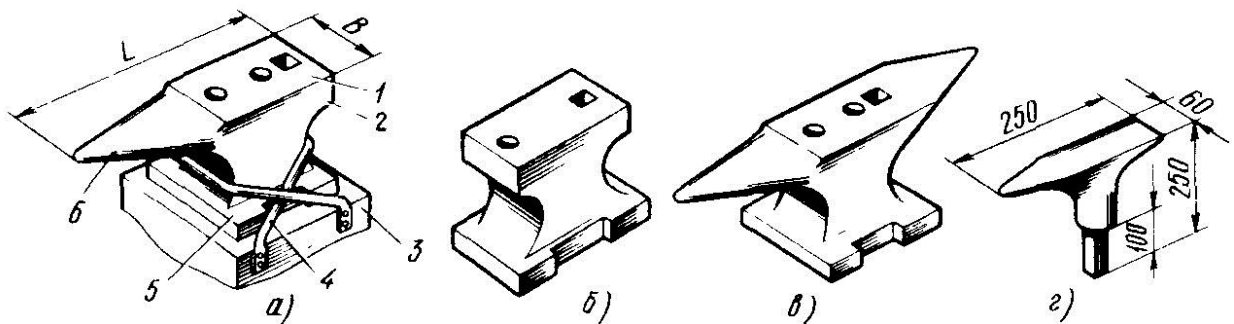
Опорний інструмент (ковадла) для ручного кування
